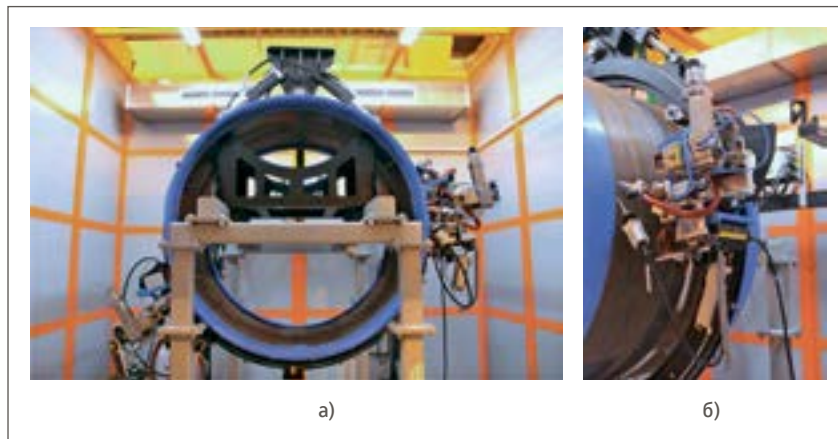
Оборудование для лазерной сварки труб: а) общий вид; б) сварочная головка
